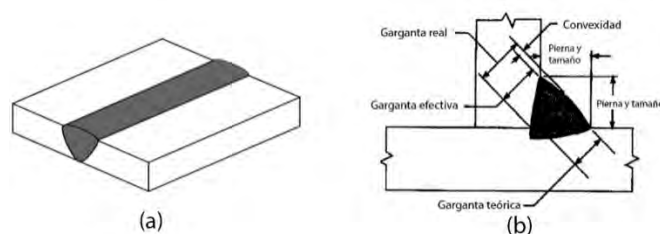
Soldadura de (a) ranura y (b) filete [5]
